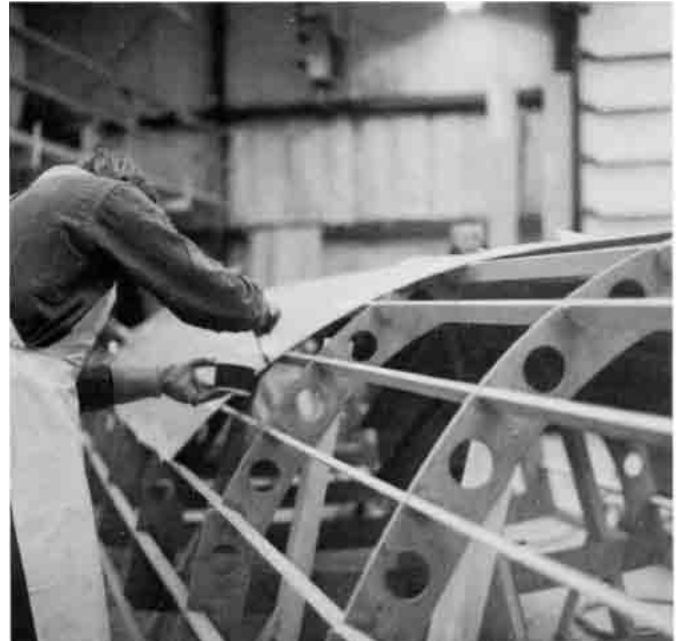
Auftragen von Harz auf die Kante einer zuvor befestigten Planke.
